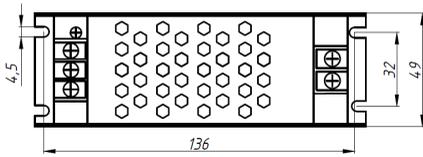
Габаритные размеры блока питания Geniled GL-12V100WM20 Slim.
